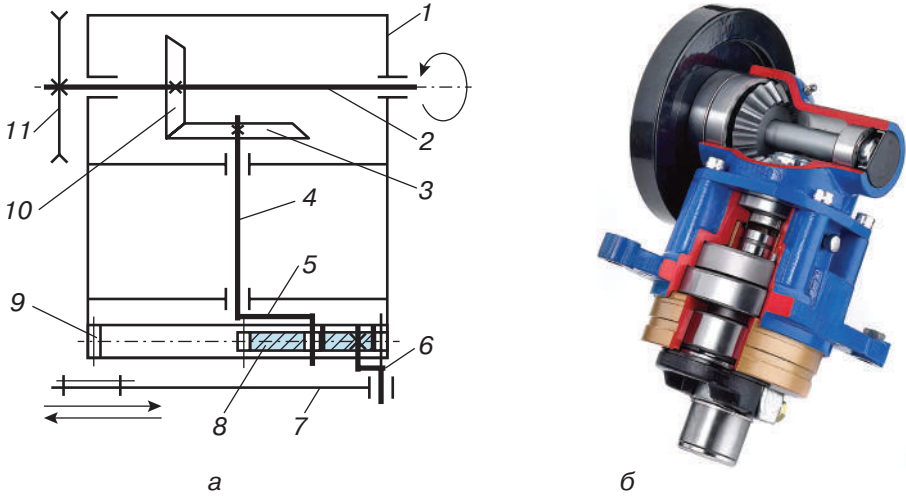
Привід ножа планетарного типу (схема а та загальна будова б):
